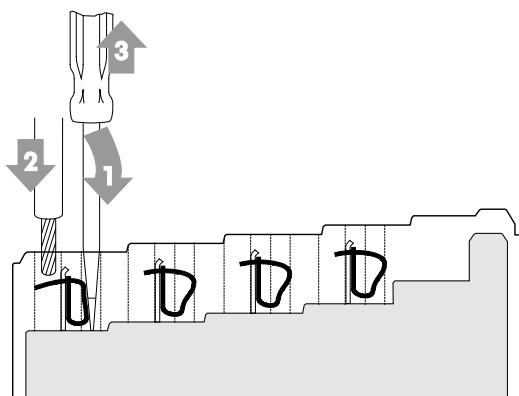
Leiter an CAGE CLAMP® anschließen
